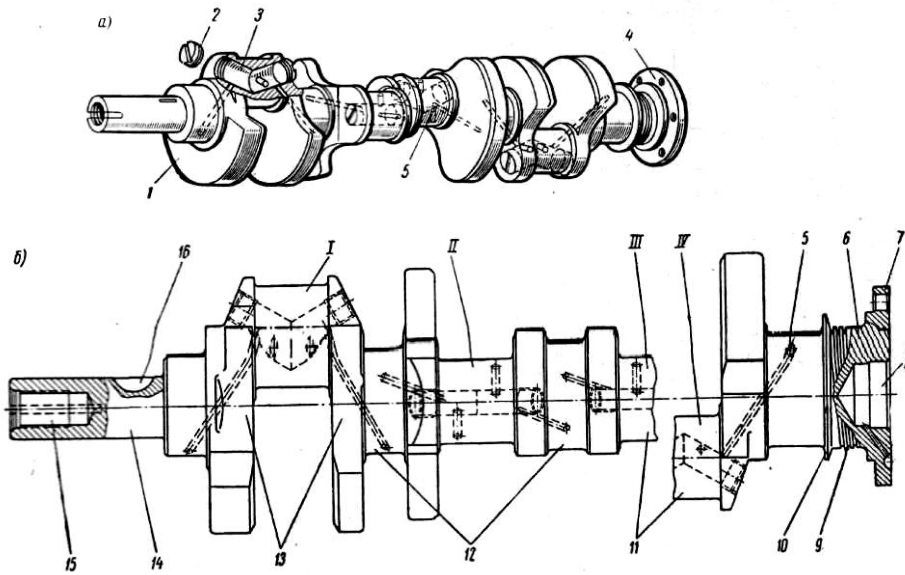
Зовнішній вигляд (а) та елементи конструкції (б) колінчастого вала V-подібного двигуна ЗІЛ: I; II; III; IV – шатунні шийки; 1 - противаги; 2 - різьбова пробка; 3 - різьбовий отвір; 4 - отвори для кріплення маховика; 5 - отвори для оливи; 6 - хвостовик; 7 - фланець; 8 - гніздо під опорний підшипник вала КЗШ; 9 - оливозгінна різьба; 10 - оливодвідний буртик; 11 - шатунні шийки; 12- корінні шийки; 13-щоки; 14 – носок вала; 15- різьбовий отвір храповика; 16- шпонкова канавка
